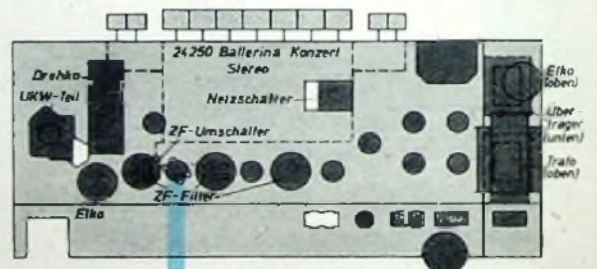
a. Chassisbestückung der Musiktube „Ballerina Konzert Stereo“
